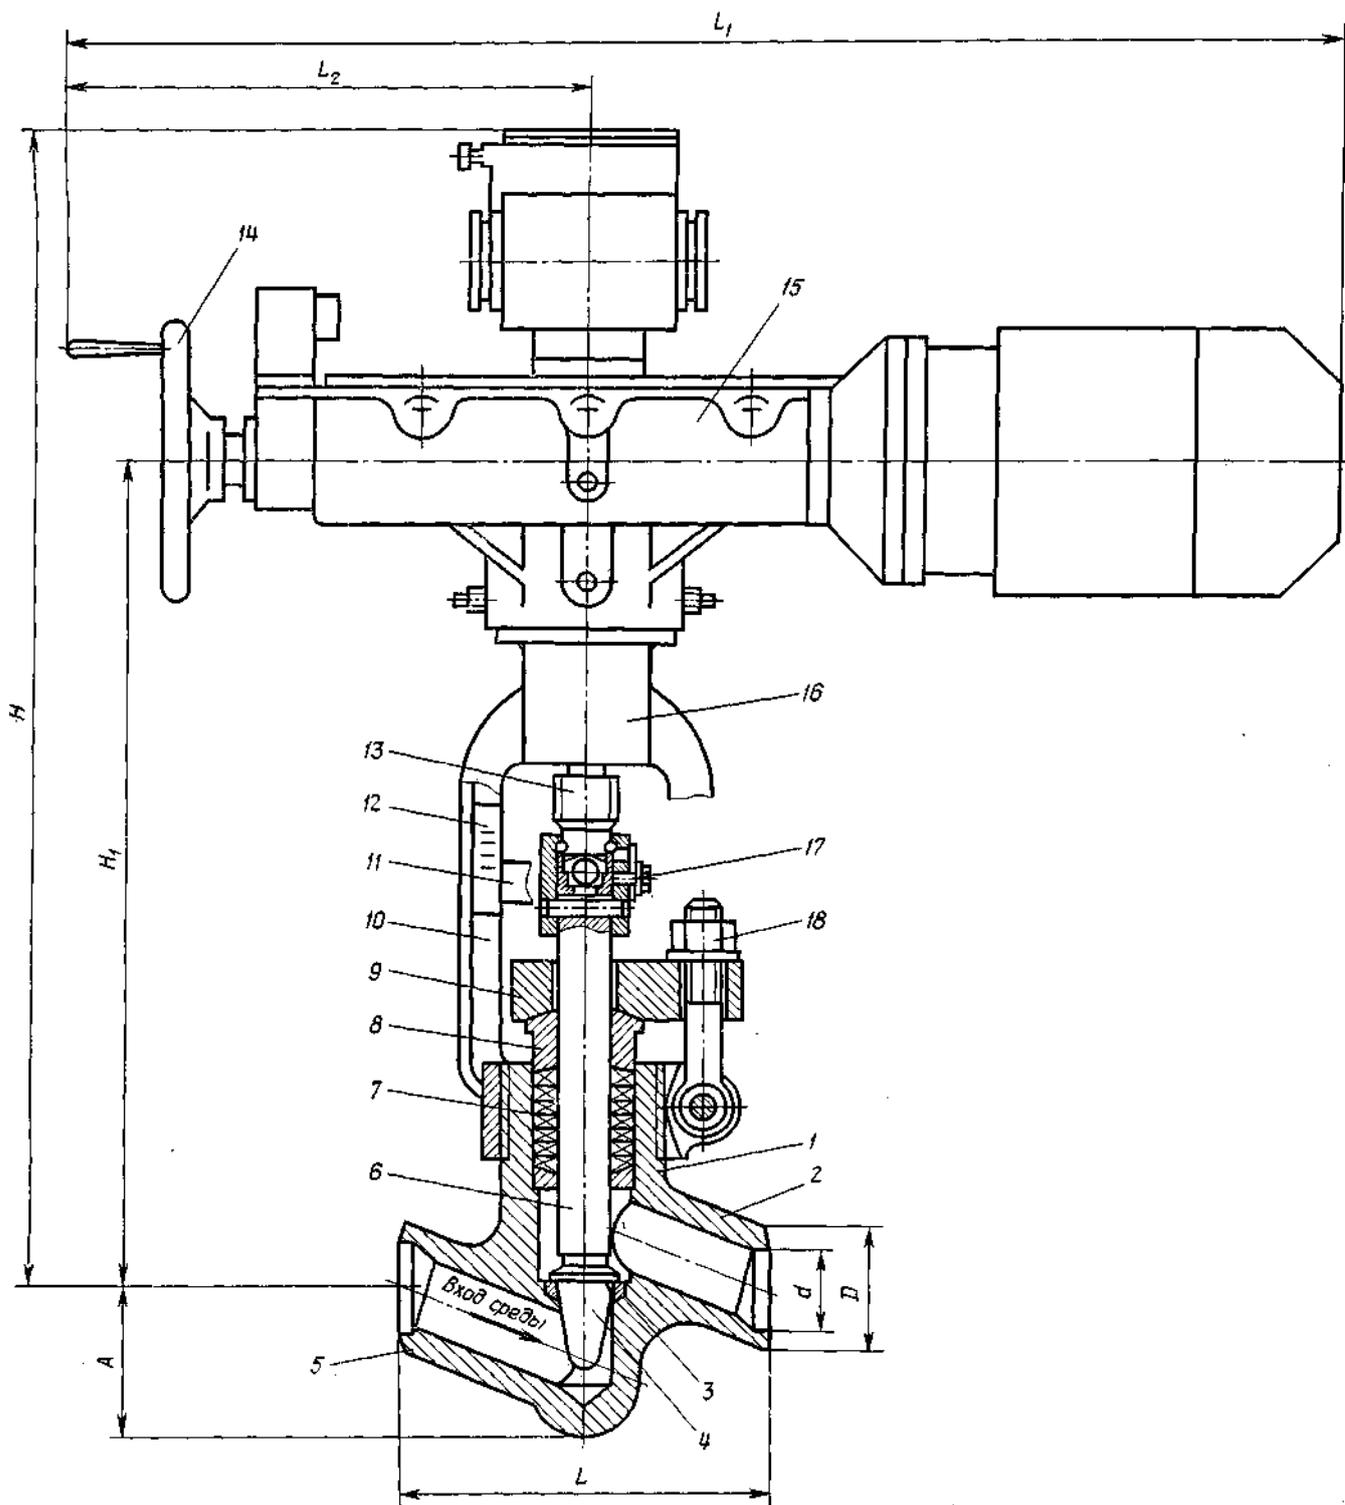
Клапан регулирующий игольчатый Dy65 серий 851, 976
